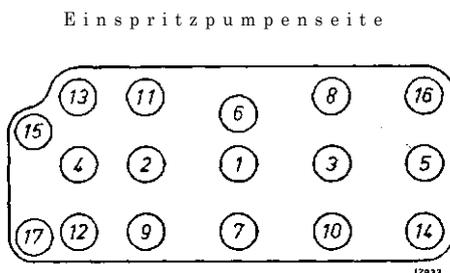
Reihenfolge für das Nachziehen der Zylinderkopfschrauben
